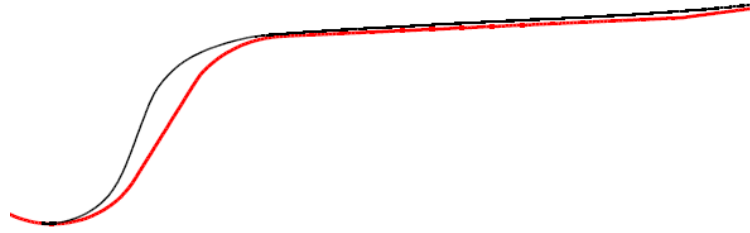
Робоча частина середньозношеного обода колеса з початковим стандартним профілем
